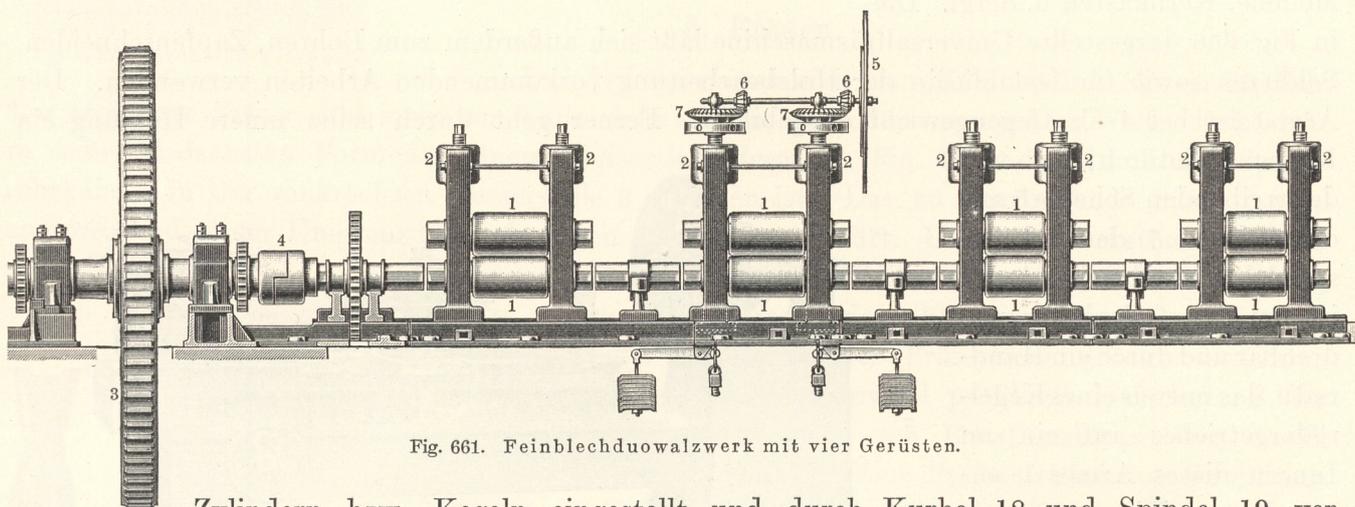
Feinblechduowalzwerk mit vier Gerüsten.
